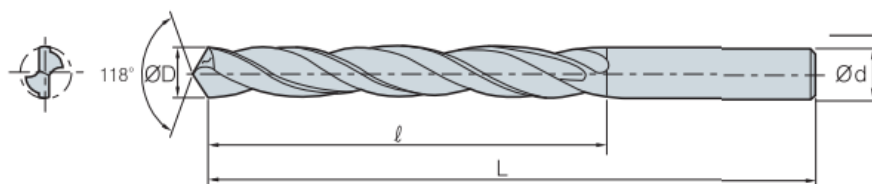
KORLOY Carbide Drill-SSD 015
